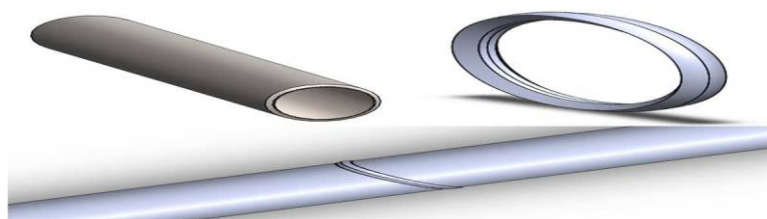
La géométrie de pipe, cordon de soudure et l'assemblage
